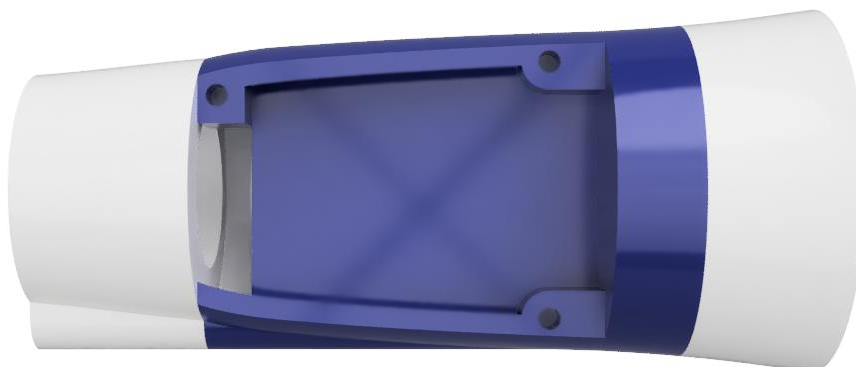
Espacio para el cableado que conecta las baterías con la placa.
